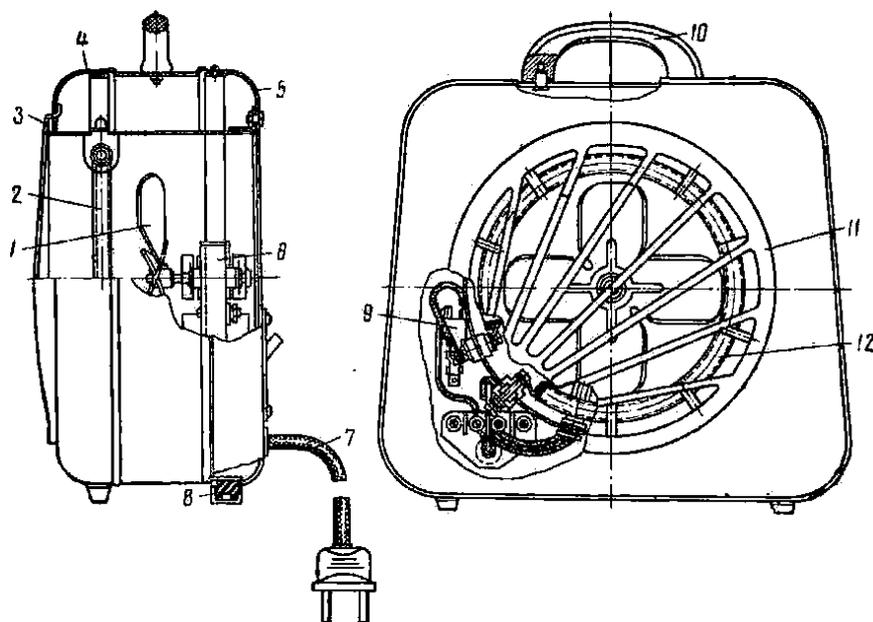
Тепловентилятор ТВ-1; 1 - крыльчатка; 2 - спираль нагревательного элемента; 3 - кожух; 4 - корпус; 5 - крышка; 6 - электродвигатель; 7 - соединительный шнур; 8 - ножка; 9 - выключатель; 10 - пластмассовая ручка; 11 - предохранительная решетка; 12 - нагревательный элемент
